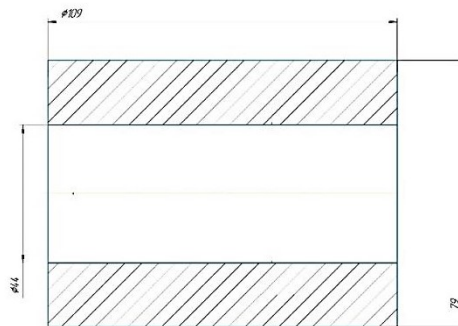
Ескіз заготовки із круглого прокату
